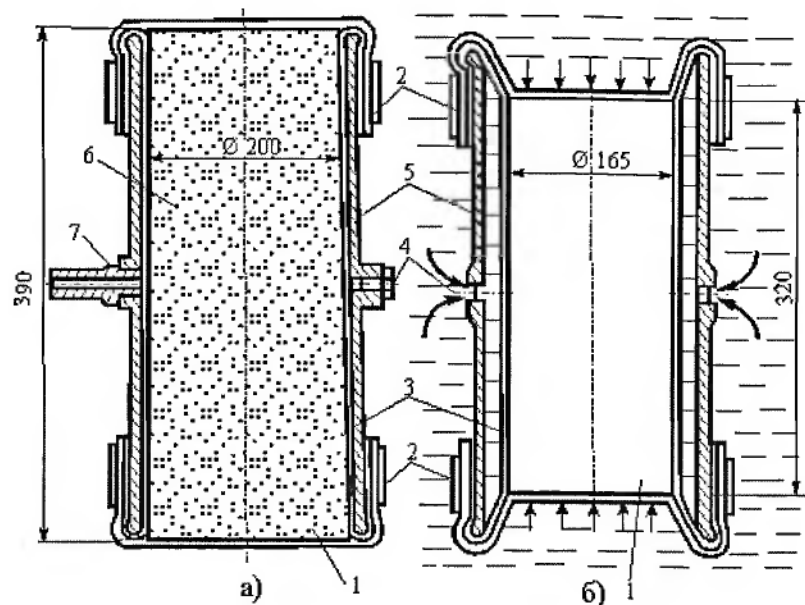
Схематичний розріз прес-форми для гідростатичного пресування циліндричної заготовки:
